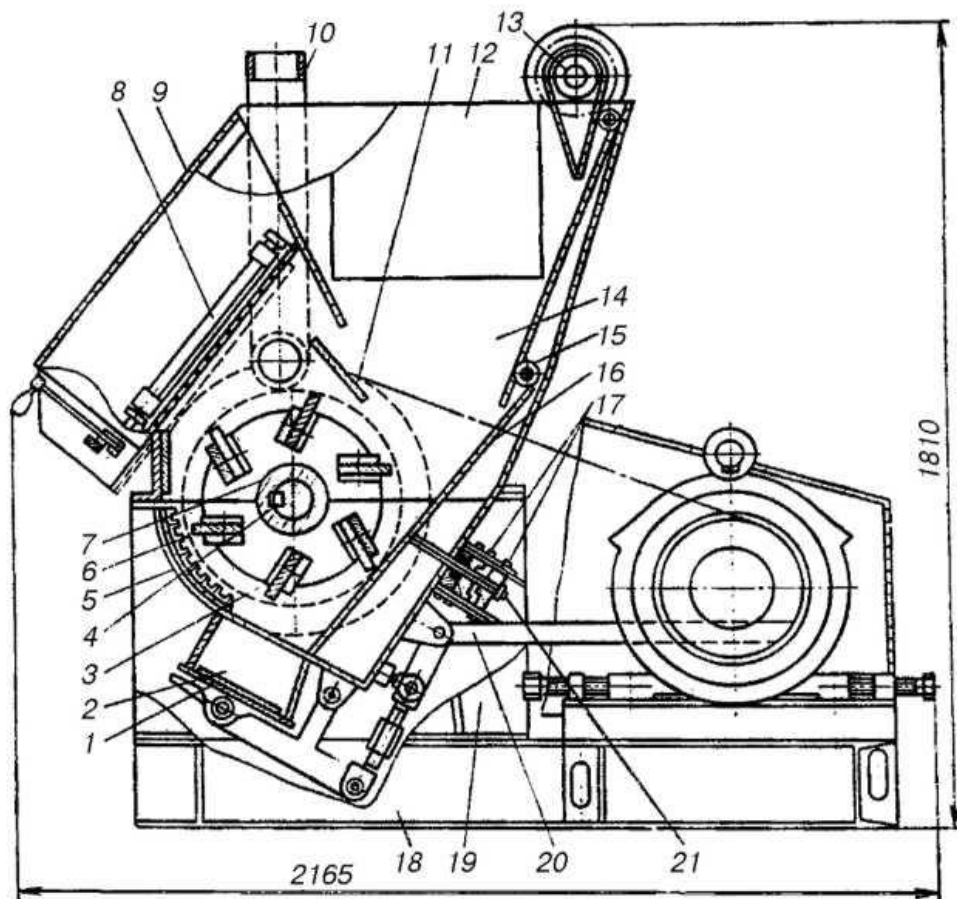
Конструкція фрезерно-струминної мішалки ФСМ-9:
